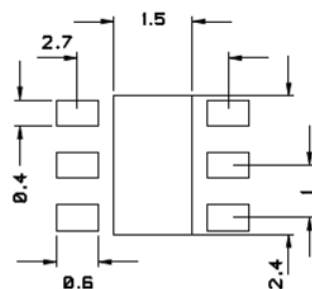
：推荐HTU21D的PCB设计尺寸。尺寸为mm
